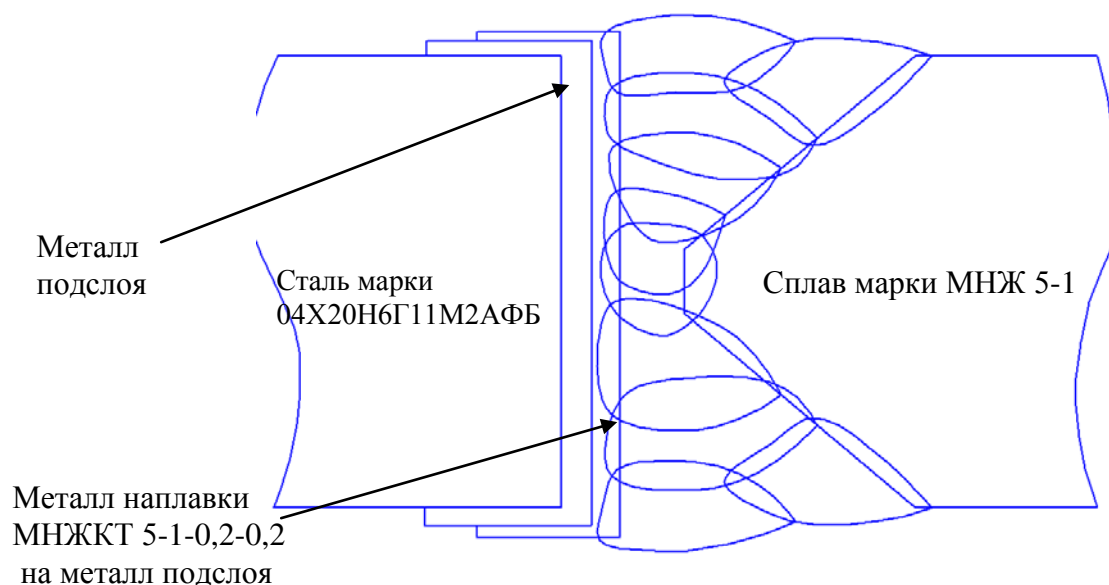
Схема сварки К-образного сварного соединения марки МНЖ 5-1 со сталью 04X20H6Г11M2AFB через подслоя, наплавленный проволокой марки ЭП-263Ш.
